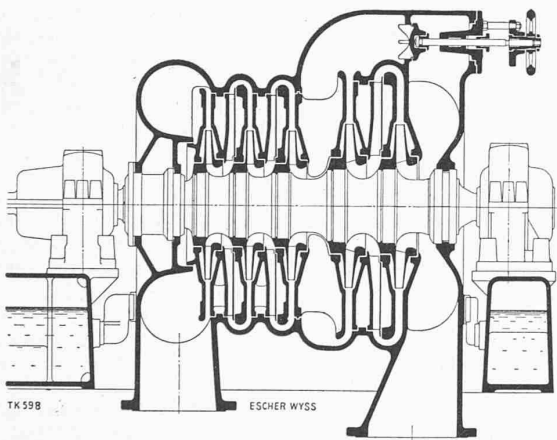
Turbokompressor mit Handventil zur Umgehung
